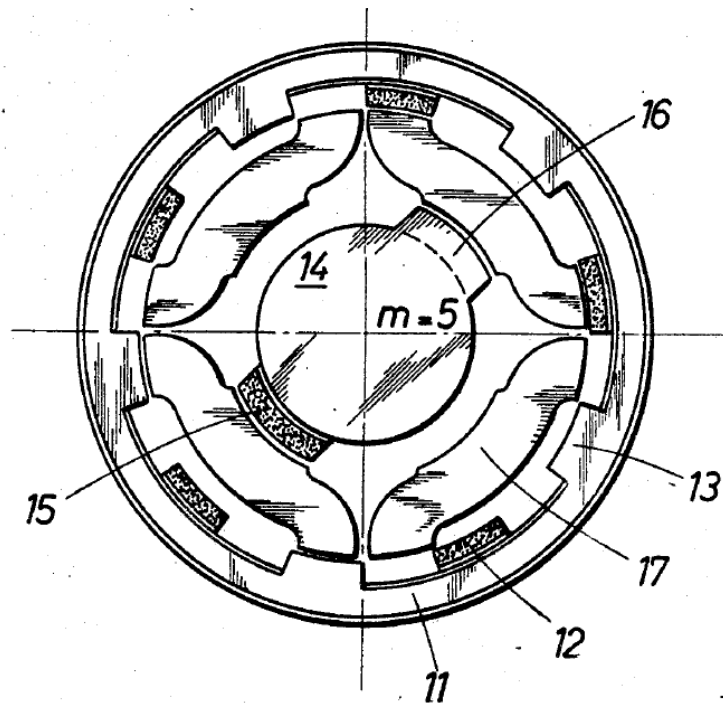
Engrenage magnétique coaxial utilisé dans [R70]
